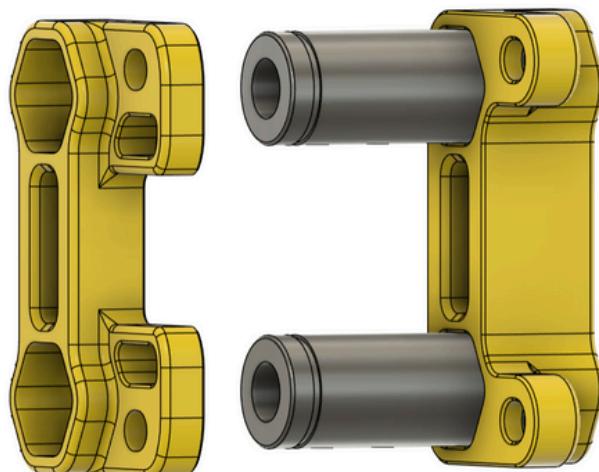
Proceso de ensamblado de los rodamientos con las piezas y_bearing_retainer.
